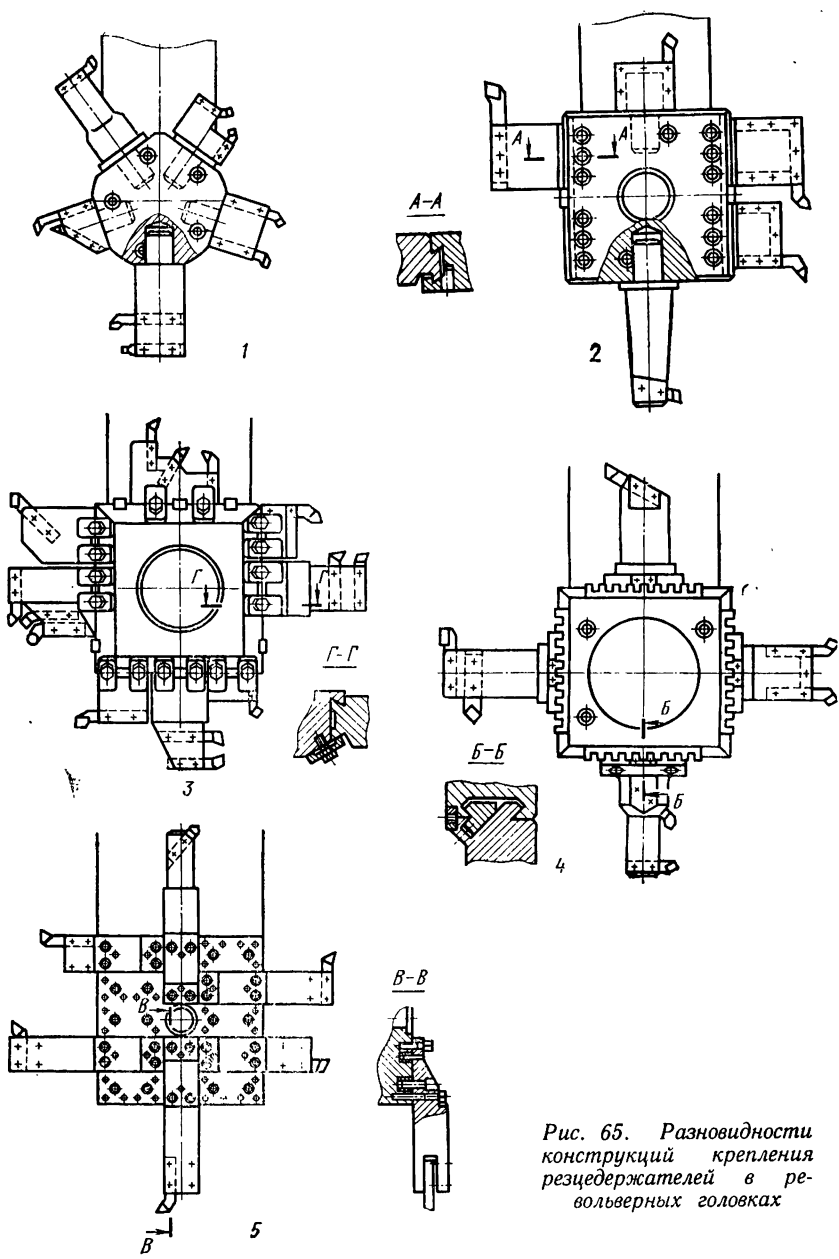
Разновидности конструкций крепления резцедержателей в револьверных головках
